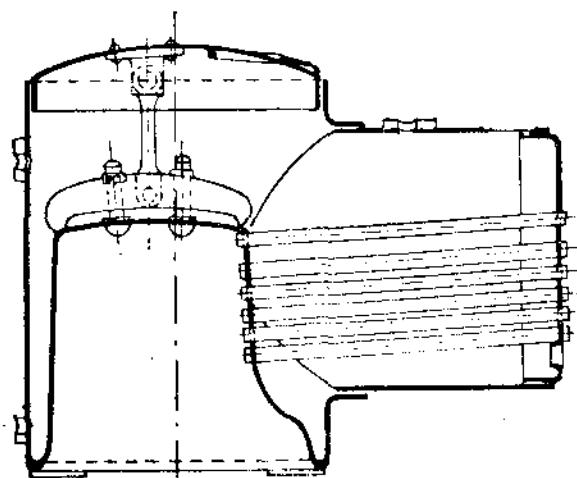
Соединение посредством сварки огневой камеры с бочкой котла.
